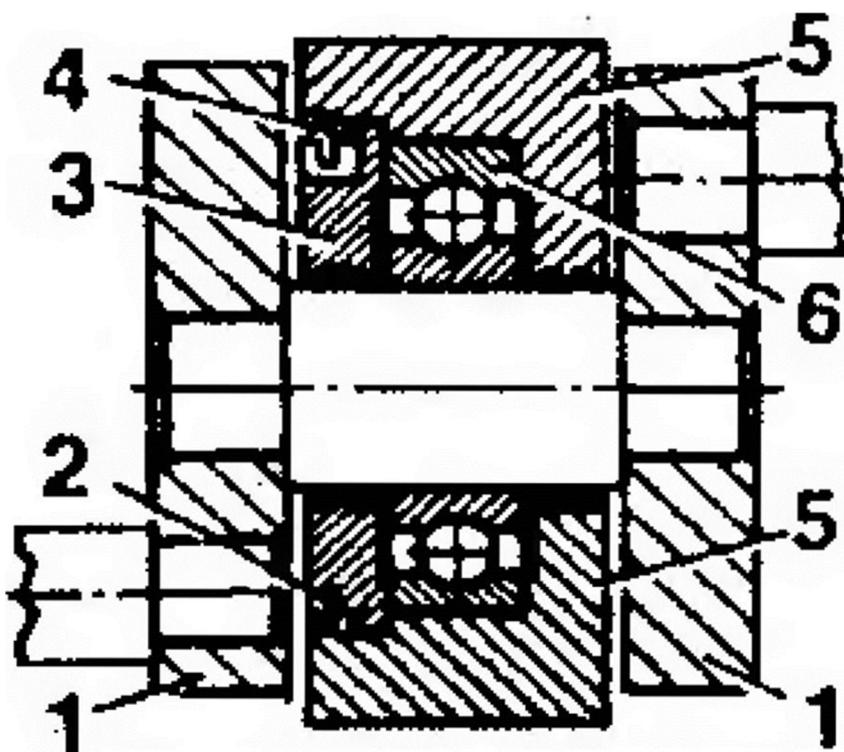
Дополнительная фиксация лабиринтного кольца в корпусе подшипника: 1 - щеки коленчатого вала; 2 - новый штифт; 3 - лабиринтное кольцо; 4 - штатный штифт, установленный на заводе; 5 - половинки корпуса подшипника; 6 - подшипник
